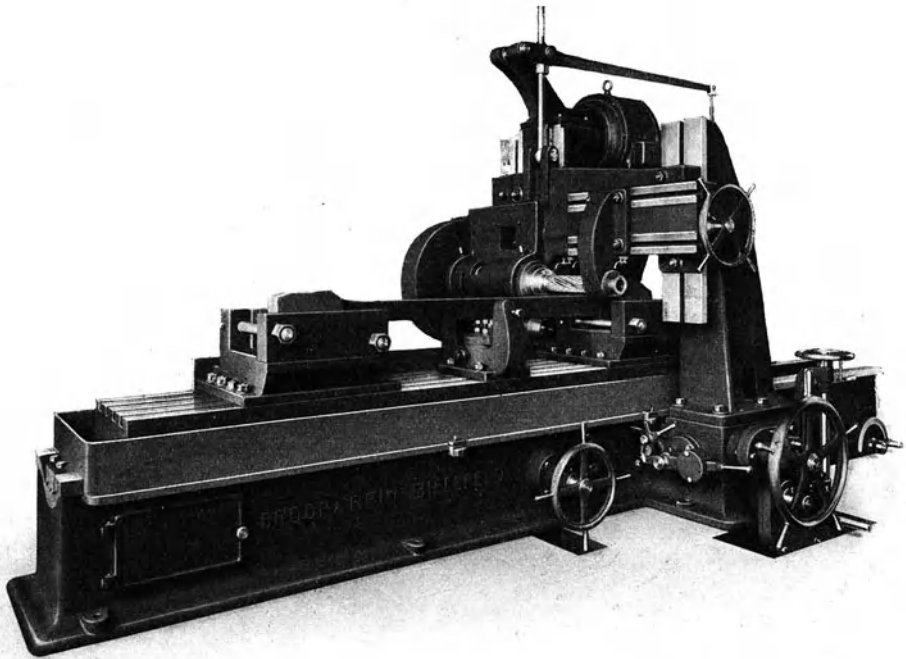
Die Langfräsmaschine von Droop & Rein.
